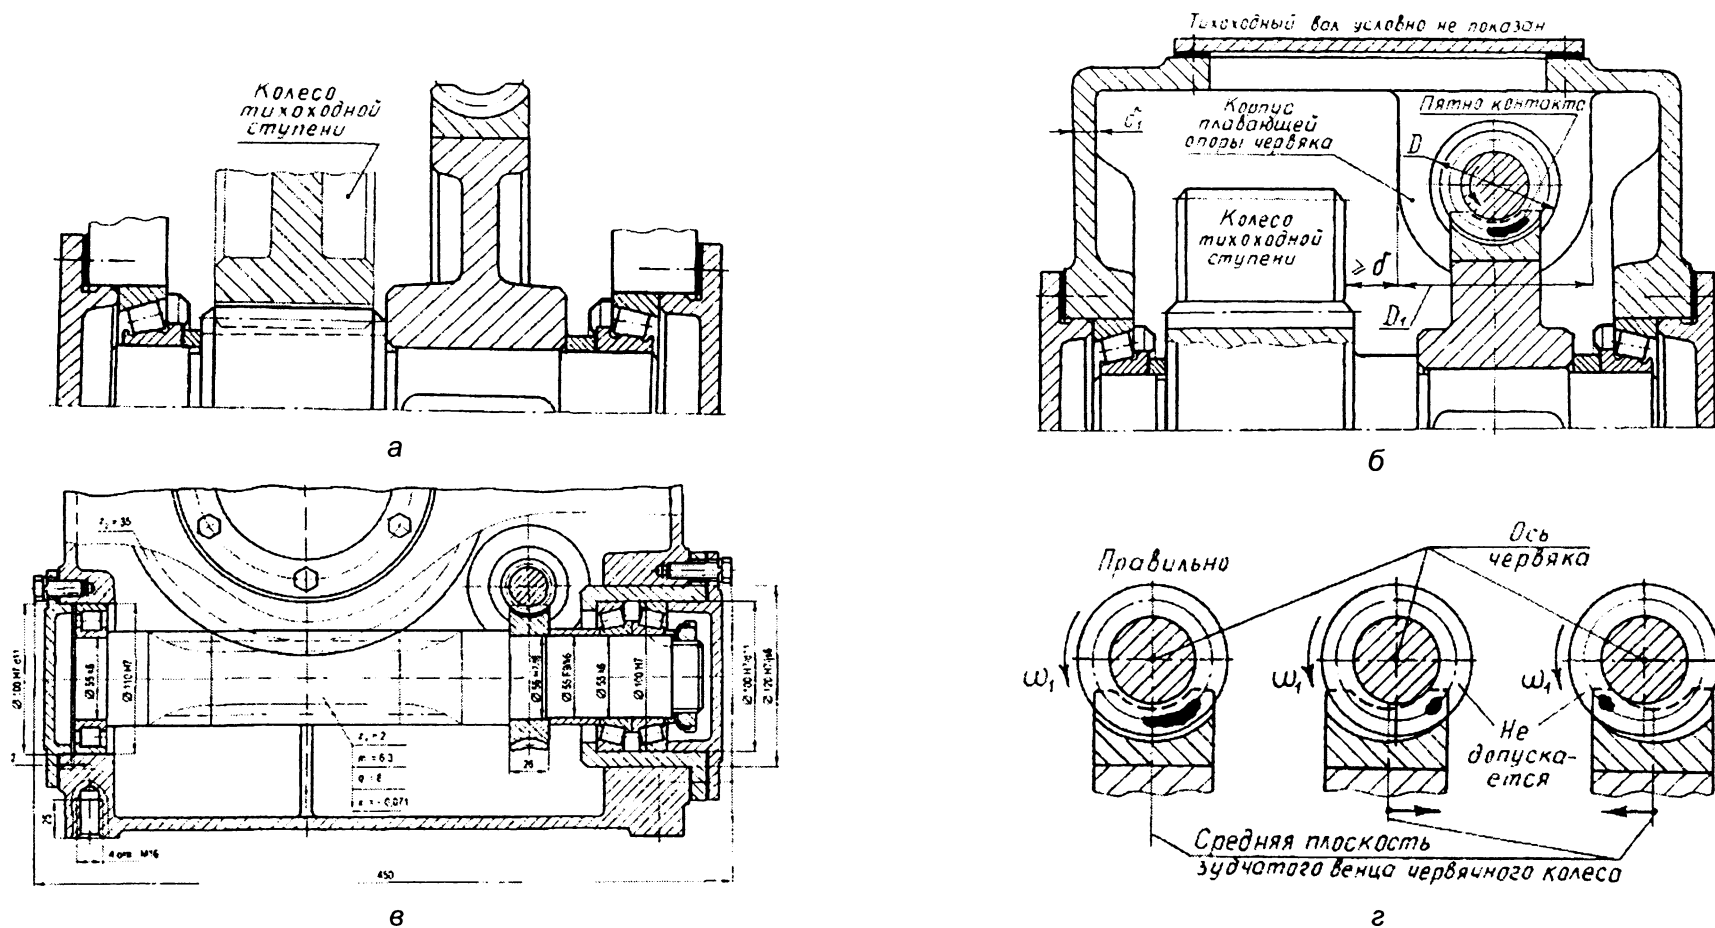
Промежуточные валы двухступенчатых редукторов с червячной передачей:
